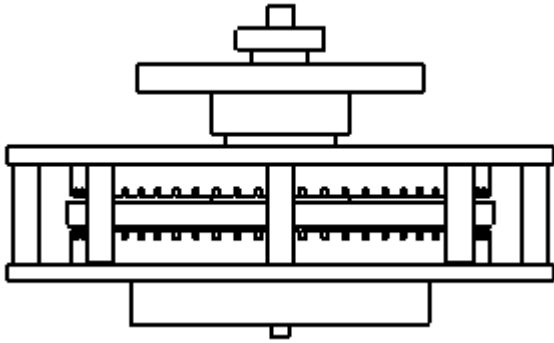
Vista lateral do CAD do gerador eletromagnético.
